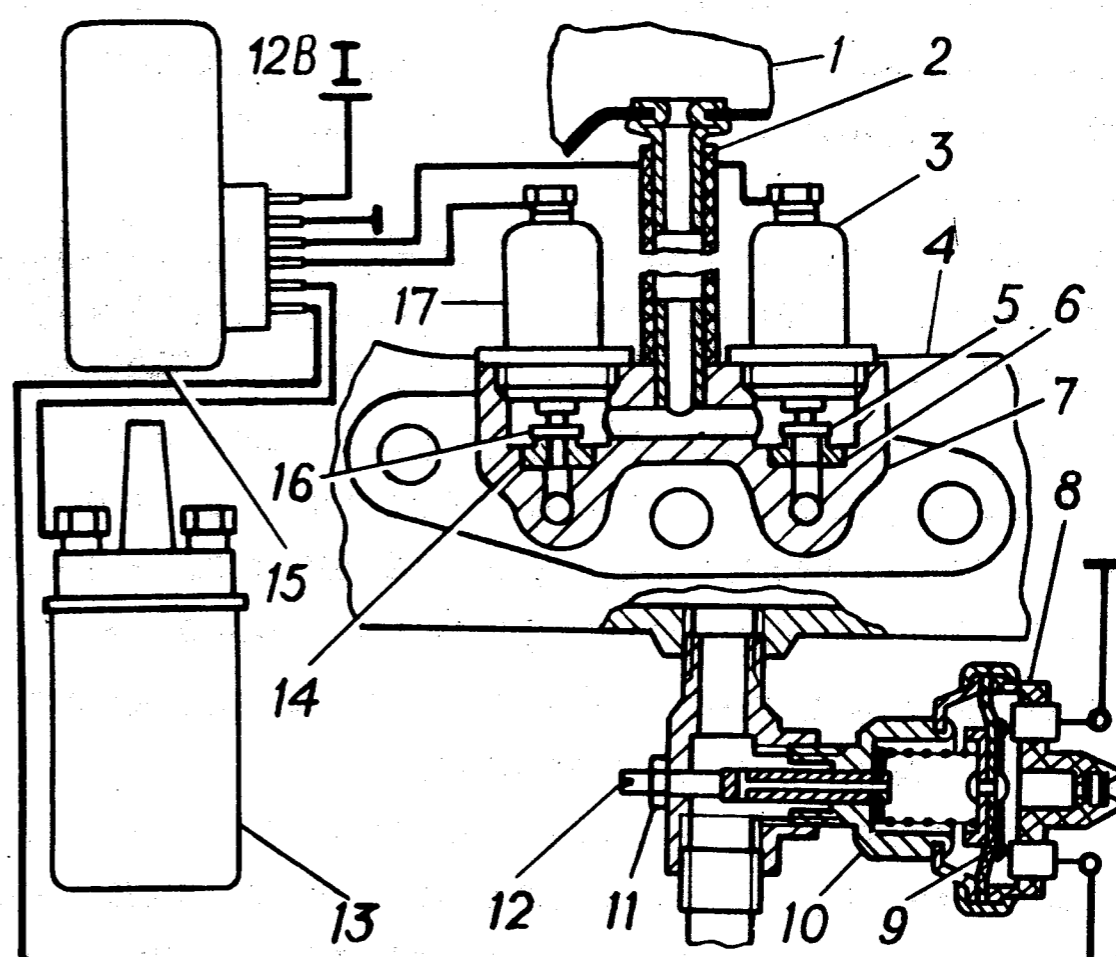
Схема системы впуска дополнительного воздуха в двигатель:
